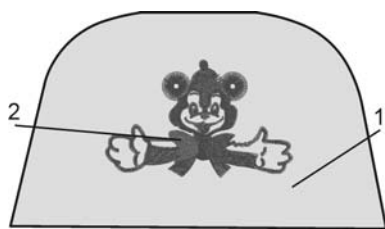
Деталь галантерейного изделия с вышивкой–
